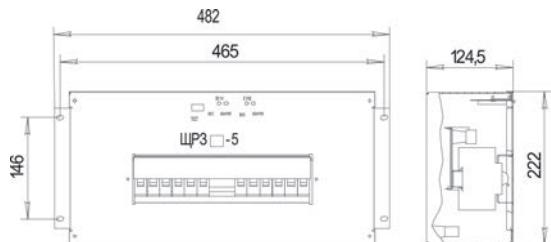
Габаритный чертеж ЩРЗ 24-5,
